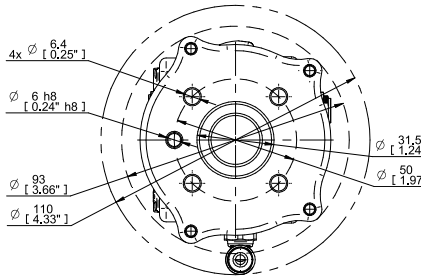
Placa adaptadora ISO 9409-1-50-4-M6. También encaja en ISO 9409-1-50-7-M6 utilizando cuatro tornillos (en lugar de siete).
